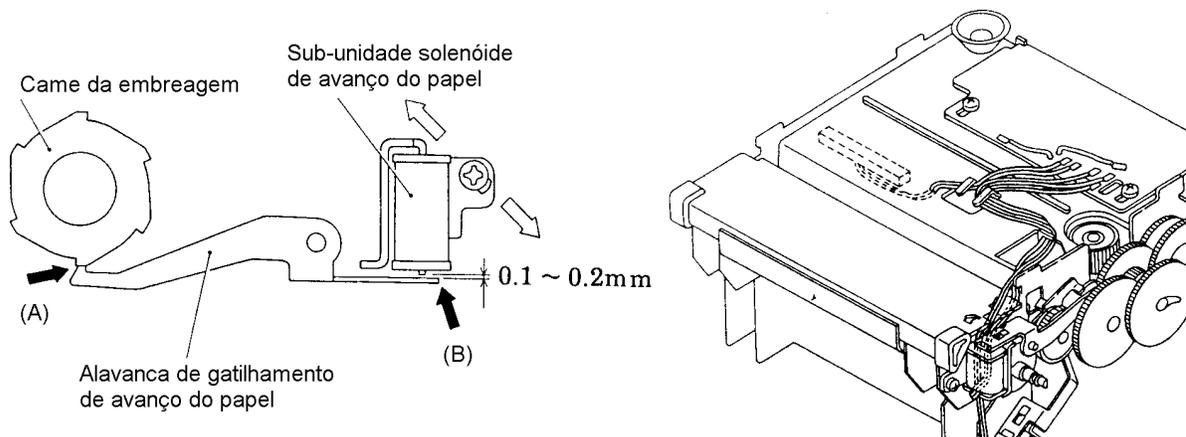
Ajuste do Solenóide de Avanço de Papel
